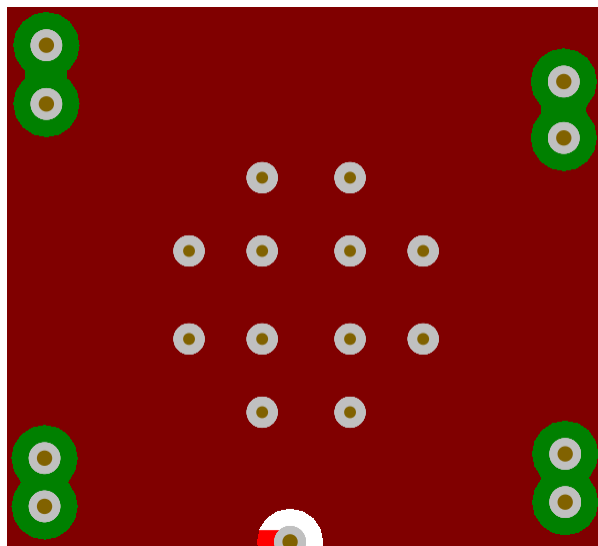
PCB Layout Example for LMK1D1212, GND Layer
